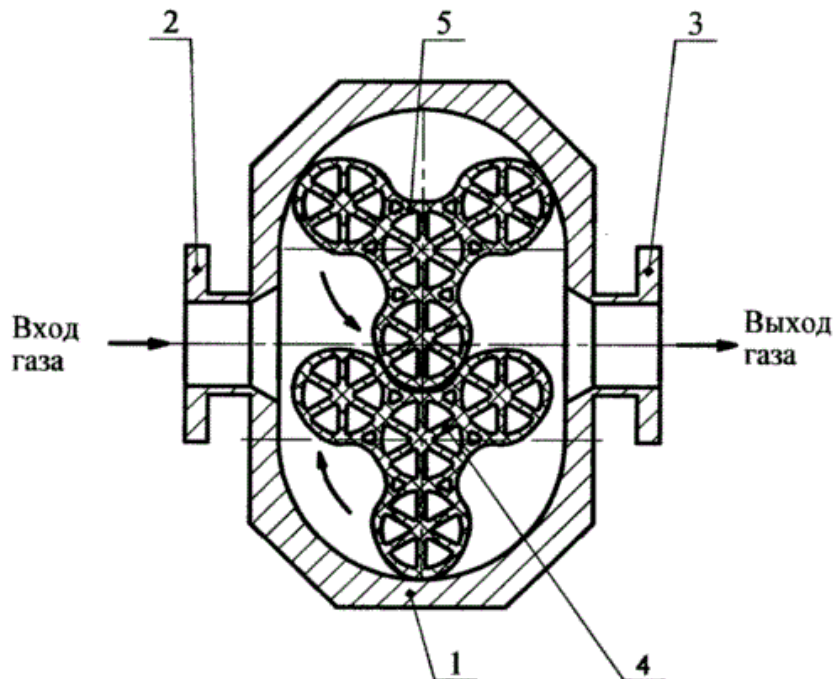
Схема роторного нагнетателя компрессора РК105/60
